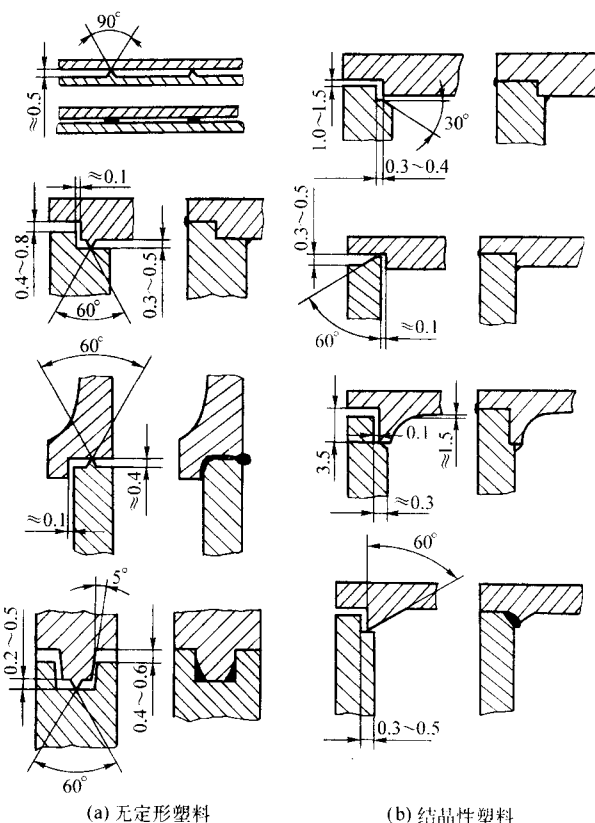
塑料超声波焊接的焊接面预加工设计举例
